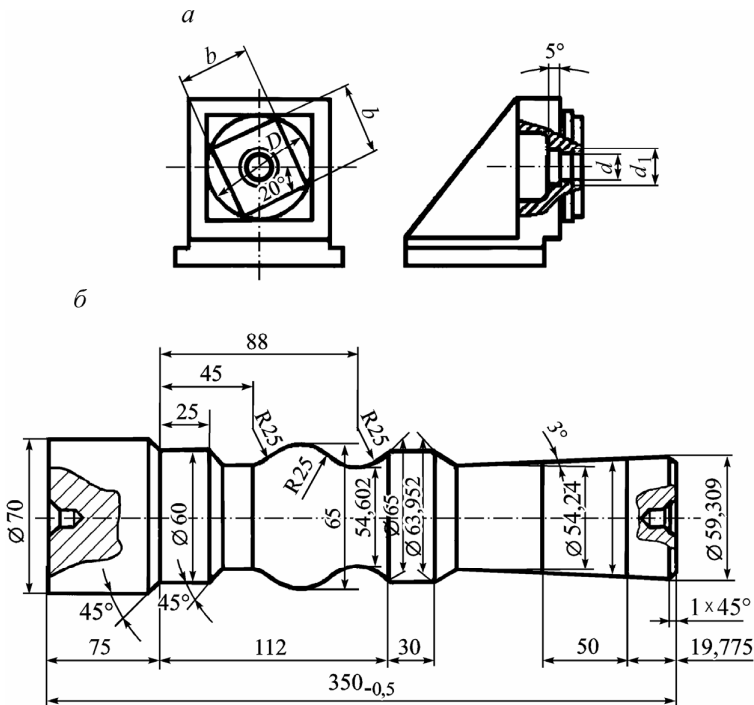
Чертеж эталона для комплексных испытаний многоцелевого станка с ПУ (а) и токарного станка с ПУ (б)
